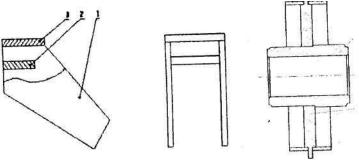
Чертежи сварных конструкций а — вилка: 1 — щека, 2 — ребро, 3 — пластина; б — колесо: 1 — корпус, 2 — диск, 3 — обод
